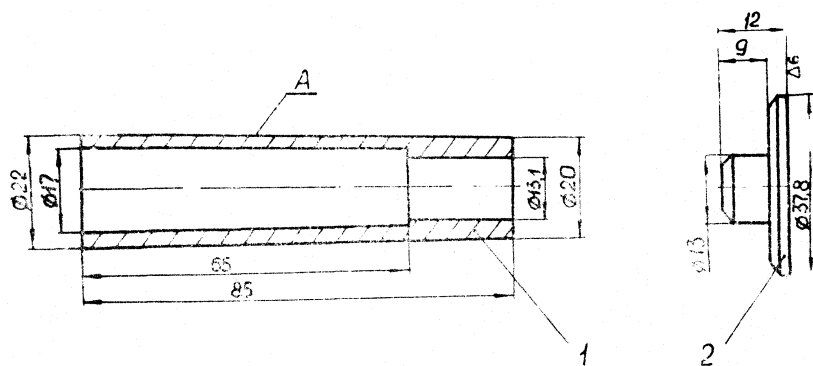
Приспособление для сборки циркуляционного насоса:
